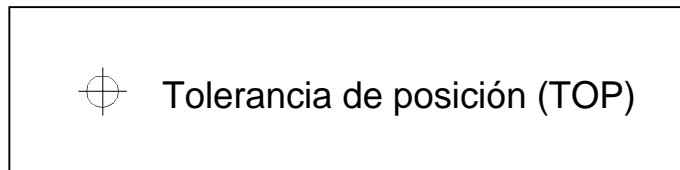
Tolerancia de Posición (TOP)
